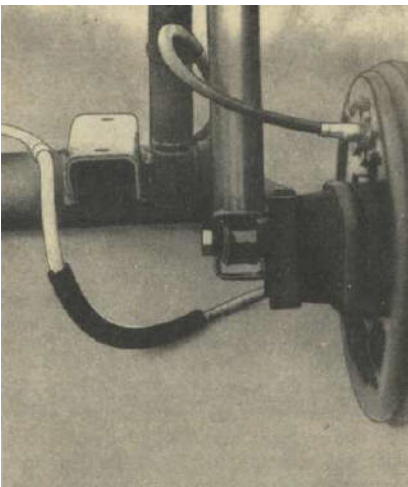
Am Schwinghebel befestigte Radbremse mit unterer Stoßdämpferhalterung, oberem Bremsschlauchanschluss am Radbremszylinder und unterer Zuführung des Handbremsseiles
